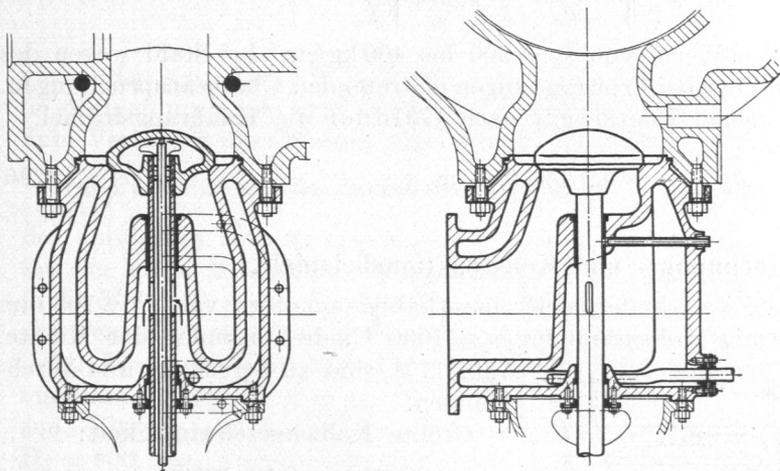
Gekühltes Großgasmaschinen-Auslaßventil, Maschinenbauanstalt Augsburg-Nürnberg.
